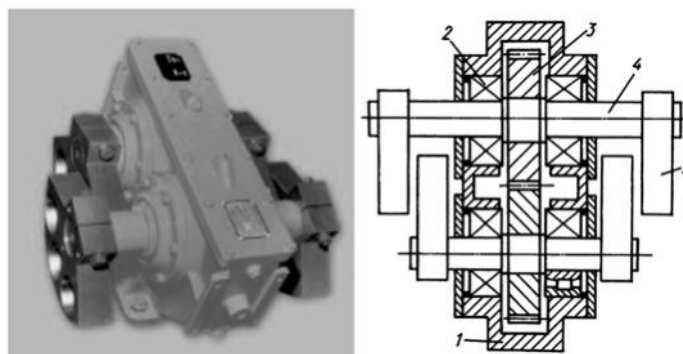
Відцентровий привід направленої дії: 1 – корпус; 2 – підшипники; 3 – зубчасті колеса; 4 – вали; 5 – дебаланси
